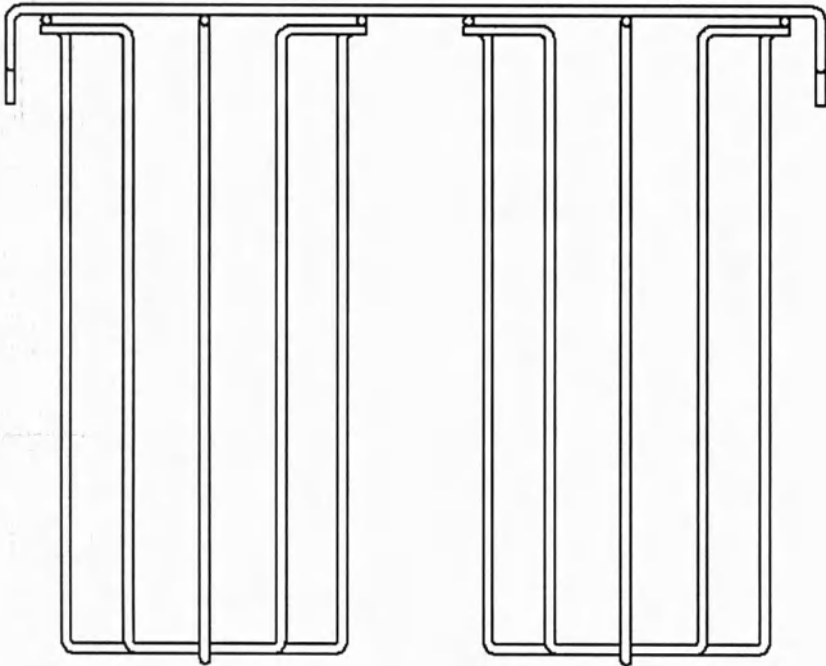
Универсальный держатель для контейнеров и флаконов
